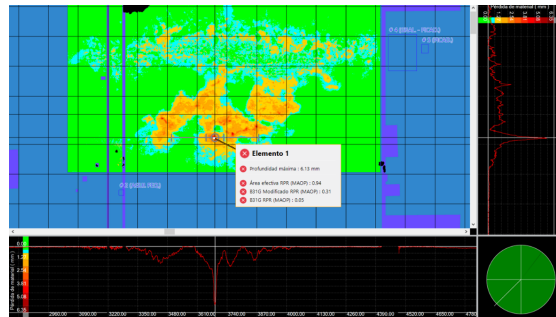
Inspección mediante las técnicas Phased Array y TOFD.
